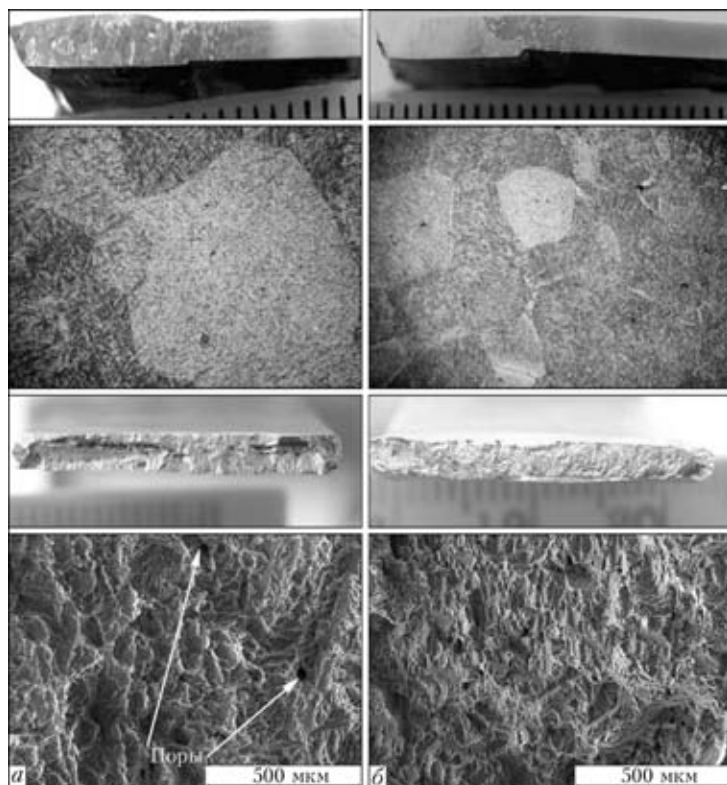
Характерный вид поверхности разрушения и микроструктура металла шва сварных соединений сплава BT8 с применением стандартных (а) и опытных (СМК) присадочных материалов из сплава BT2
